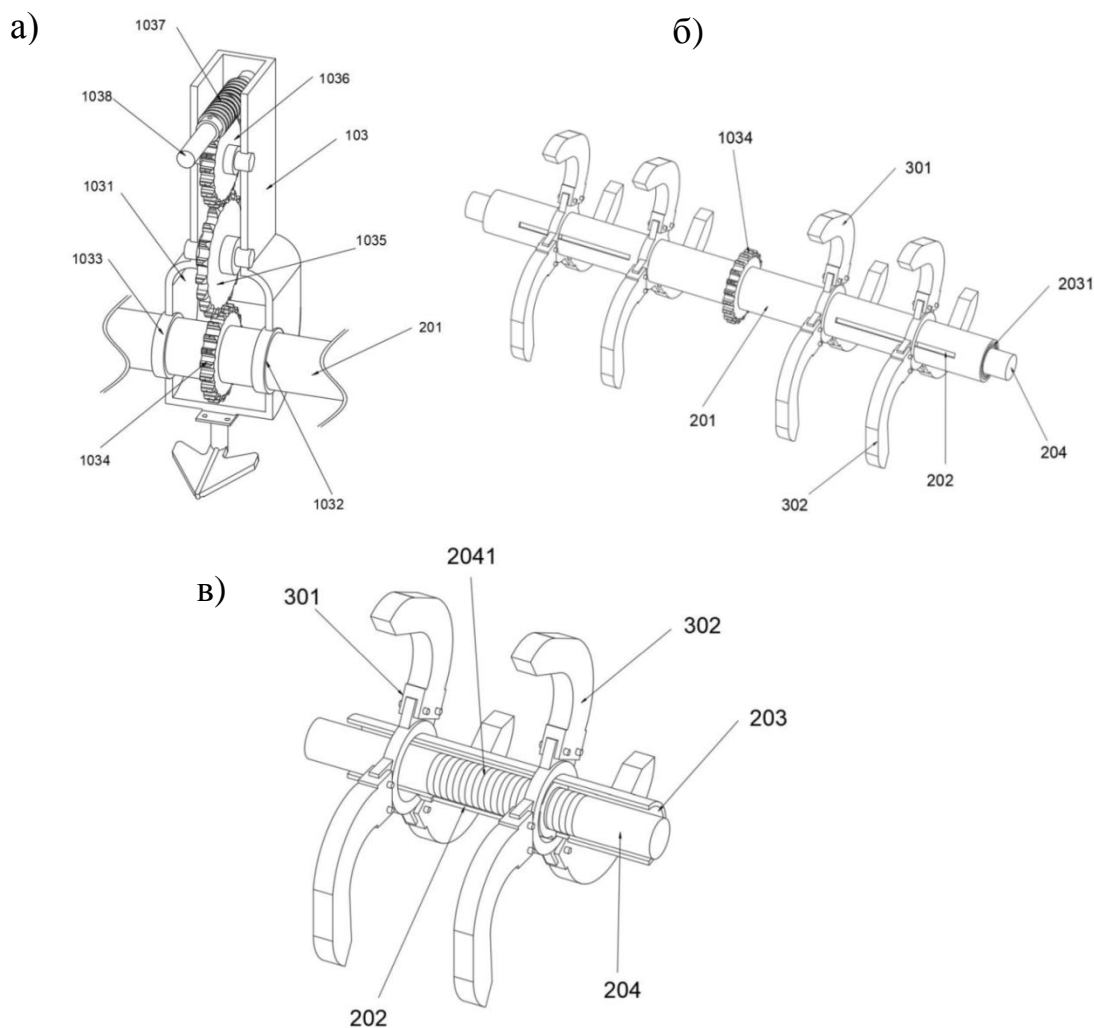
Общий вид вала фрезы с регулируемым по ширине захвата, рабочими органами: а – червячный редуктор фрезы; б - вал с рабочими органами; в – механизм регулировки расстояния между секциями рабочих органов.
